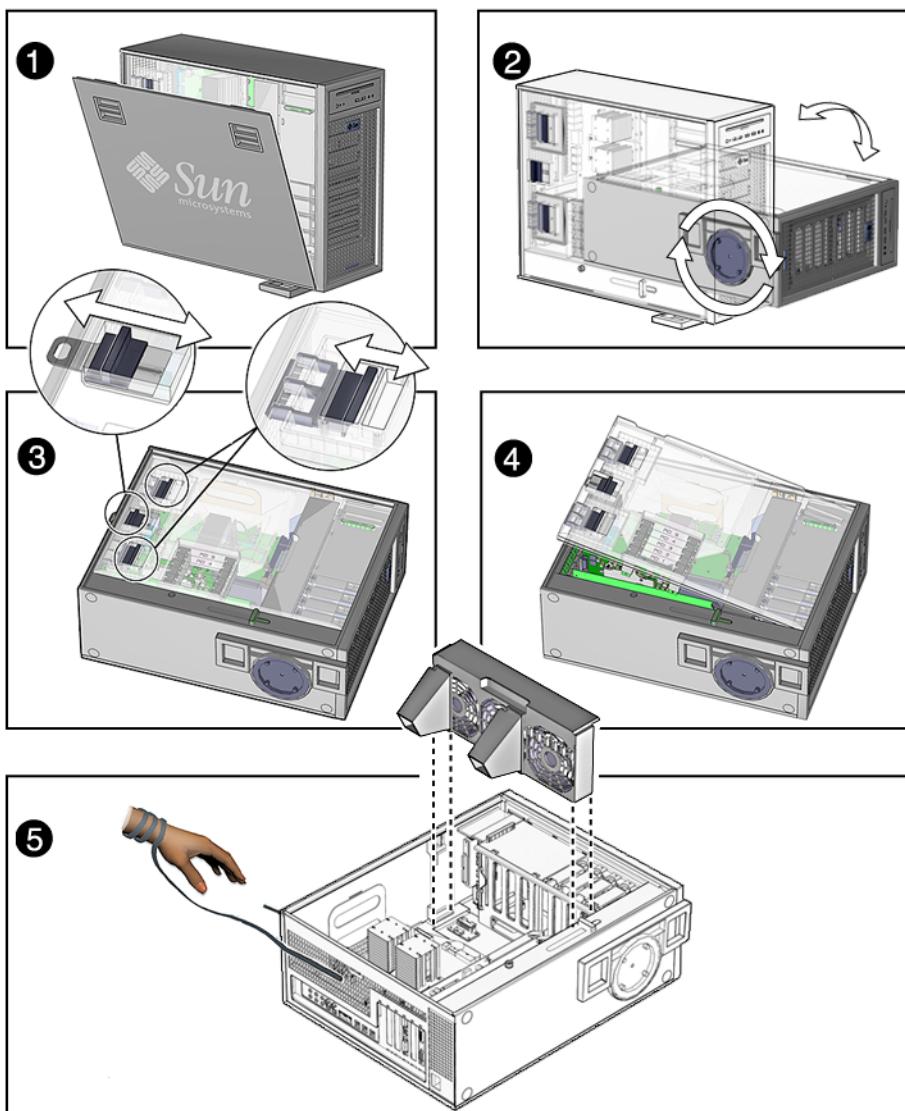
Retrait, capot latéral, panneau d'accès et module de ventilation
